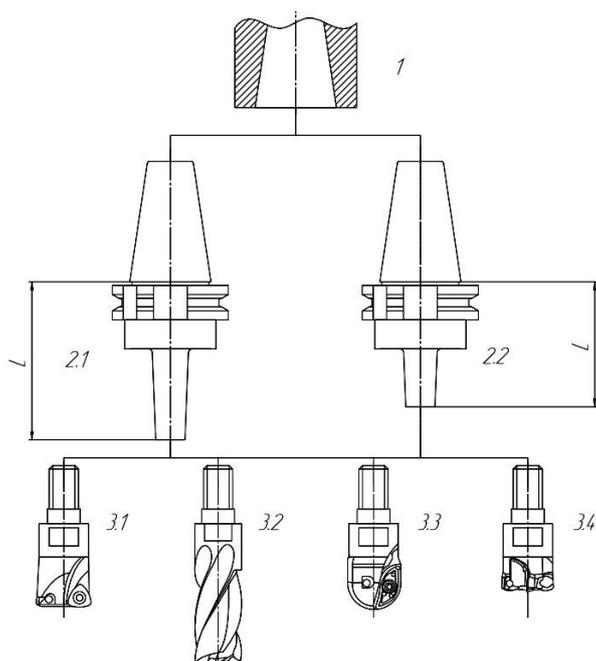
Схема сборки модульных концевых фрез и их установки на станке
